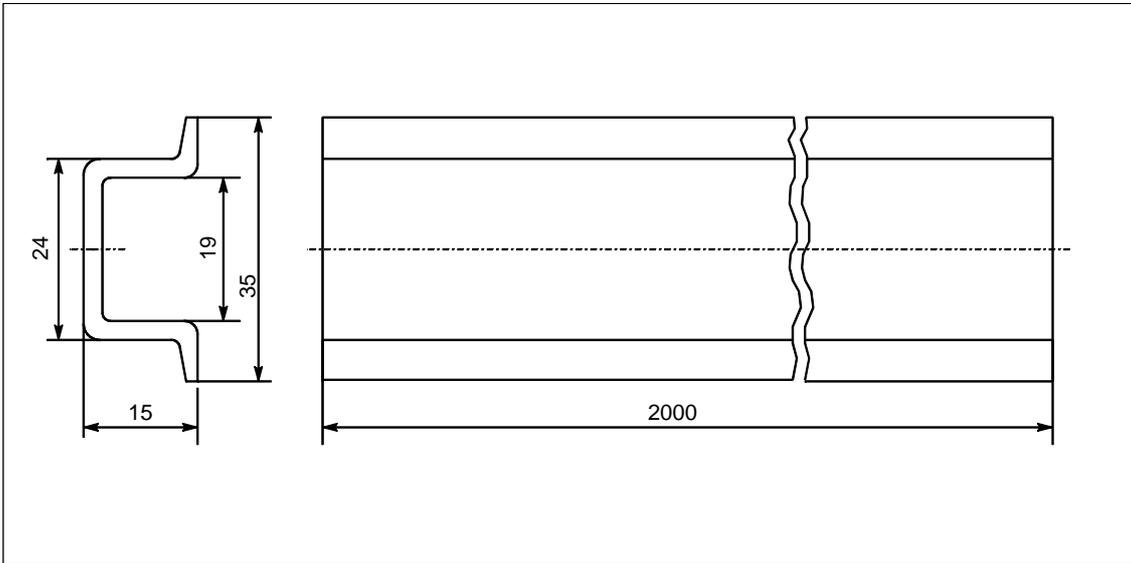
Чертеж с размерами 2000-миллиметровой стандартной профильной шины
